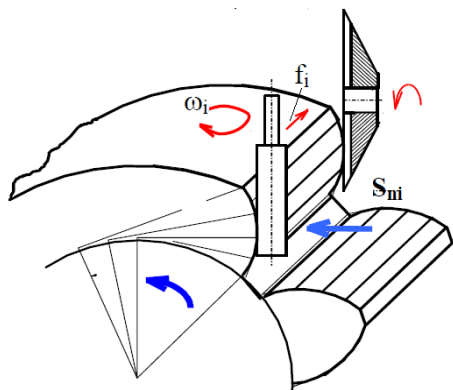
Нарязване на зъби на цилиндрично зъбно колело с палцова фреза чрез контурно обхождане [9]
